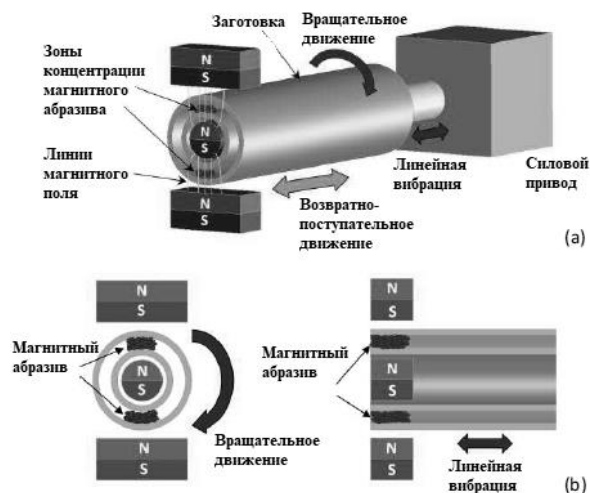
Схема метода магнитной абразивной очистки двухслойной заготовки [8]
